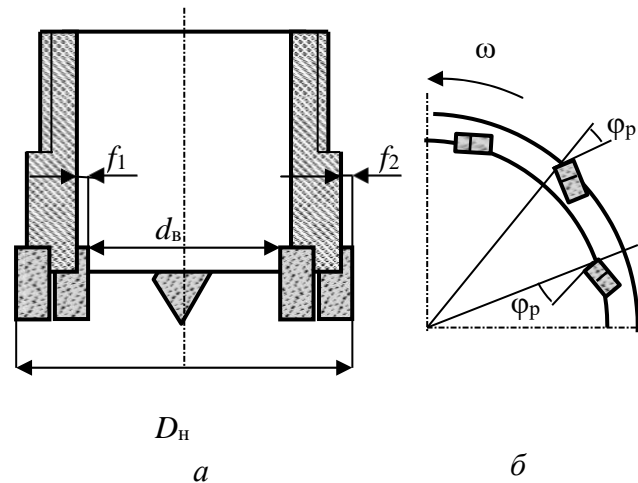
Схема вооружения твердосплавной коронки: *a* – вид сбоку в разрезе; *б* – размещение резцов на торце коронки с поворотом на угол φ_p в фронтальной плоскости резания-скалывания
